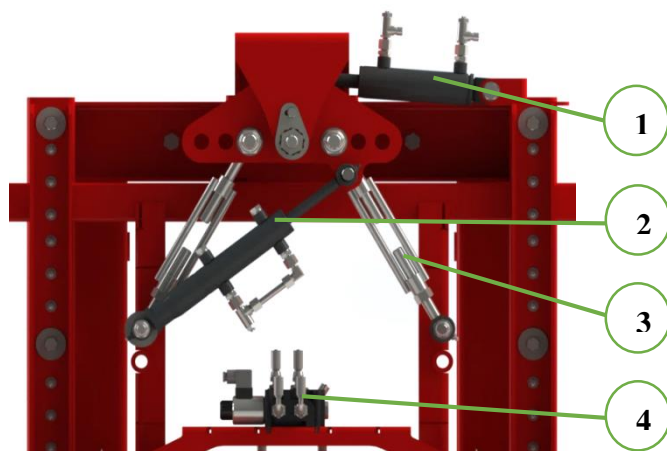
ZWEIPUNKT-AUFHÄNGUNG MIT HYDRAULIKDÄMPFUNG
